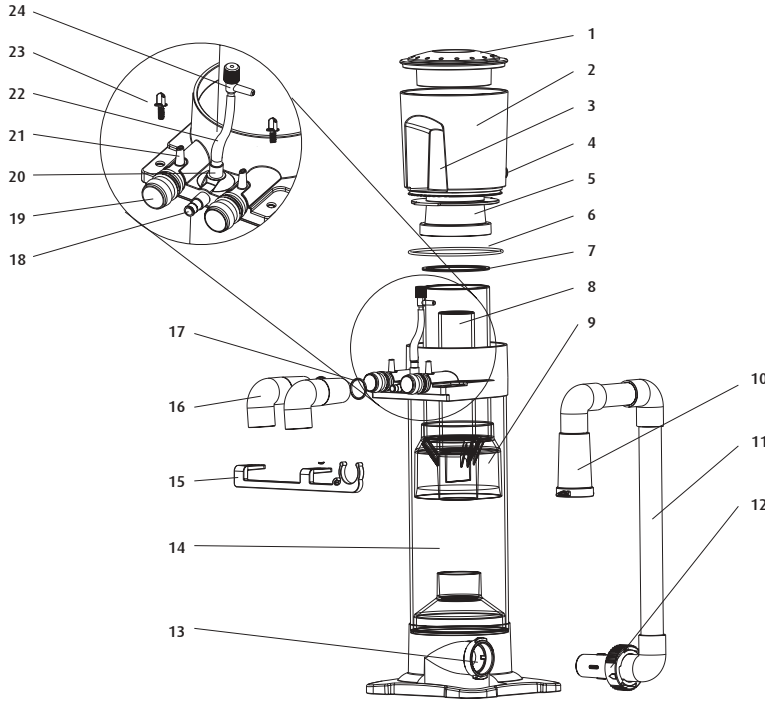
Explosionszeichnung des Berlin X2 Abschäumers
